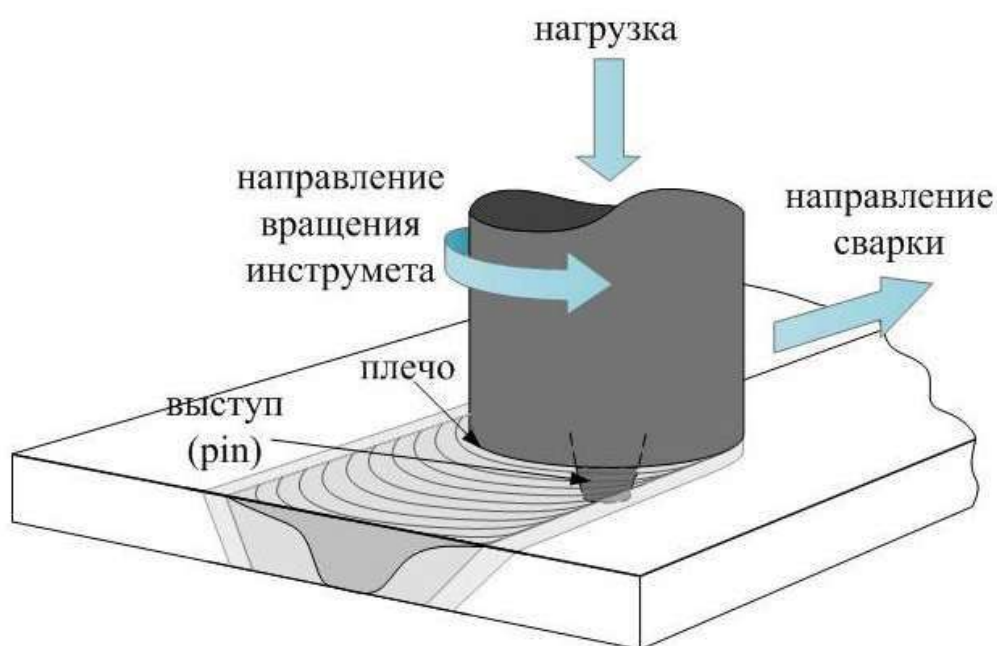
Схема процесса сварки трением с перемешиванием
